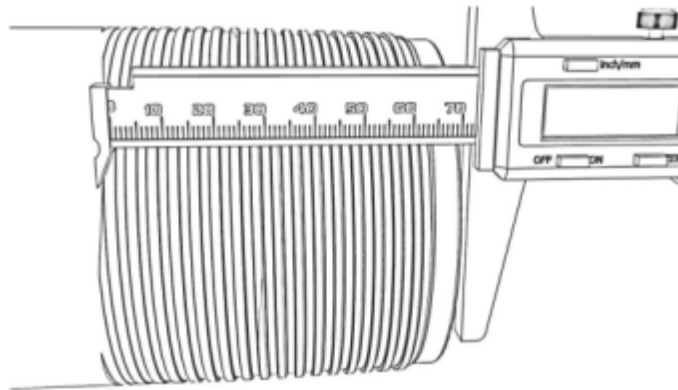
Измерение длины резьбы штангенглубиномером
